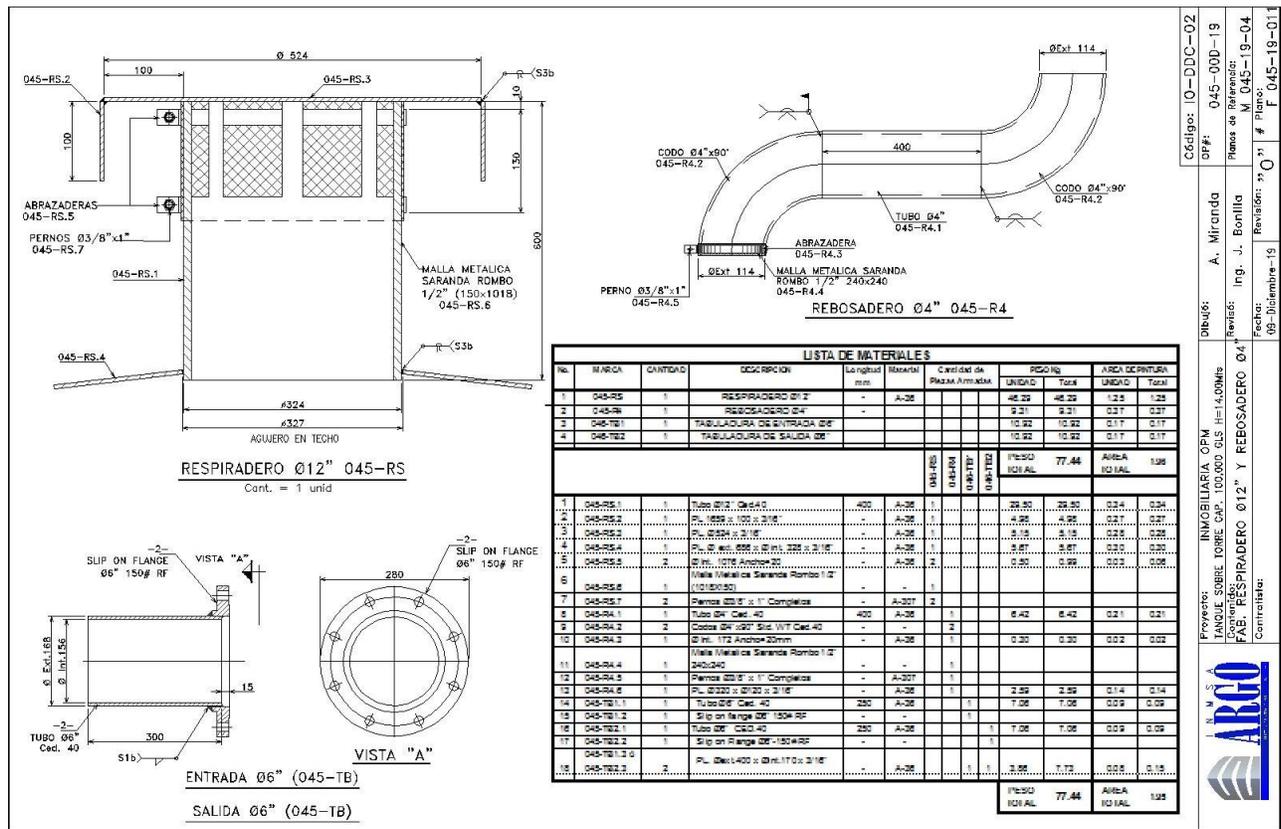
Plano de fabricación de accesorio de tanque elevado
